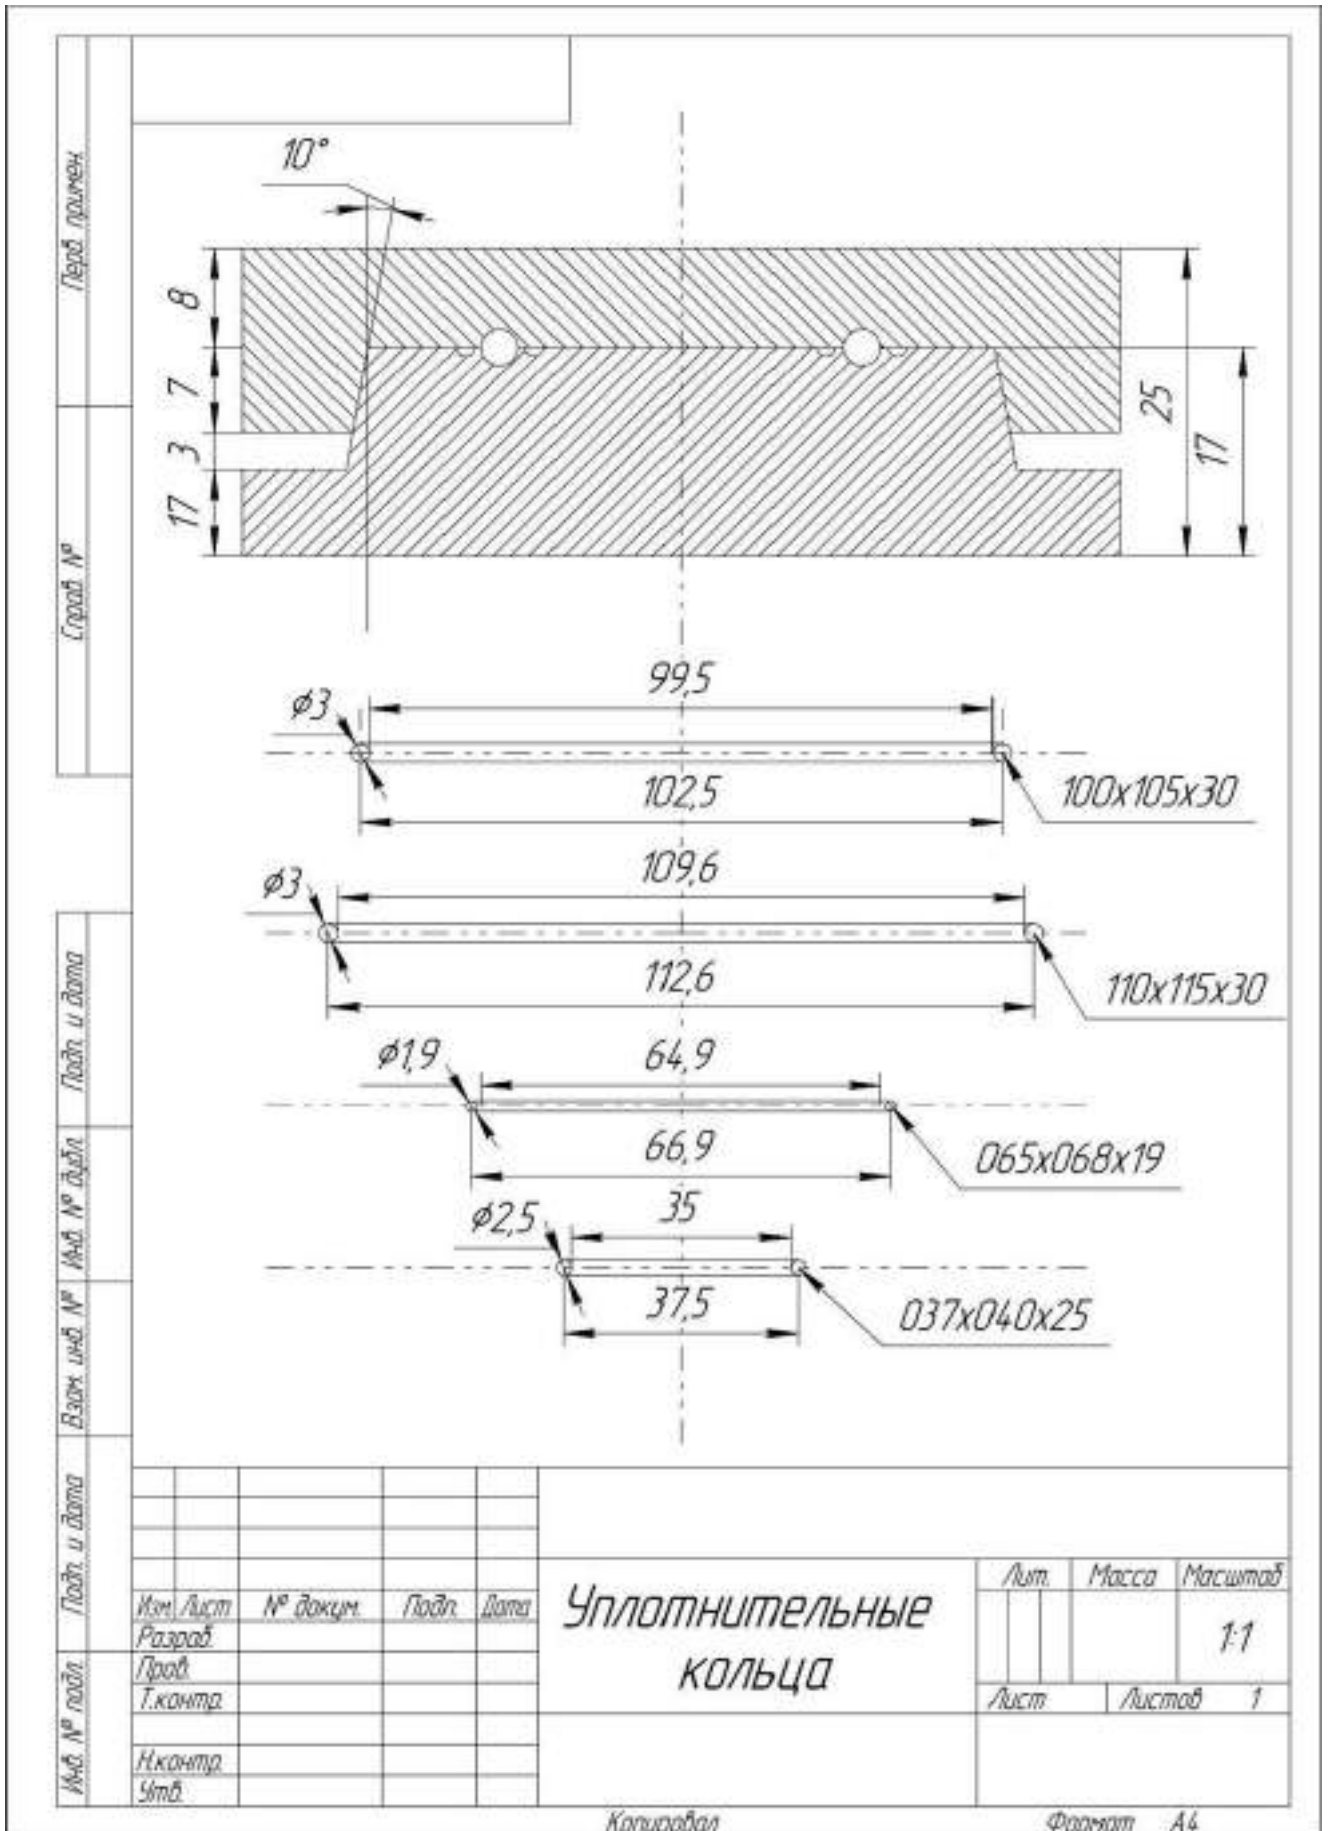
Чертеж пресс-форм для уплотнительных колец разных размеров
